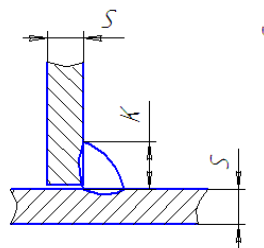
Соединение T1 -Δ5 по ГОСТ 14771-76, сварной шов №1
